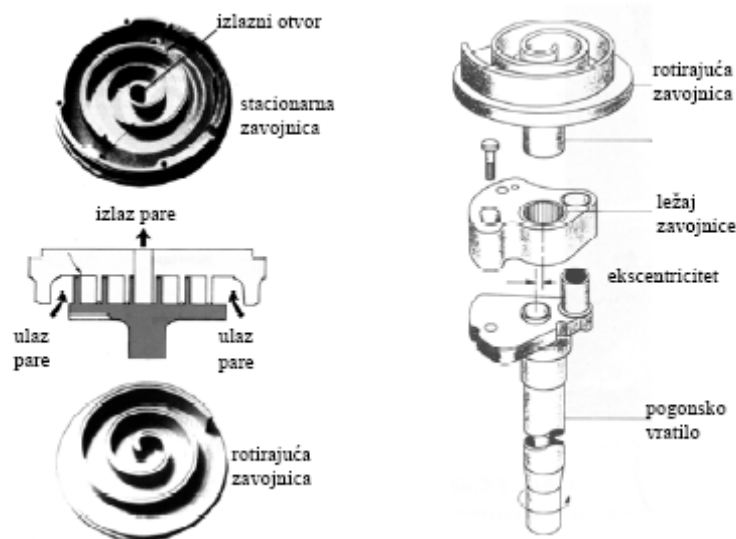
Proces kompresije u jednorotornom kompresoru
